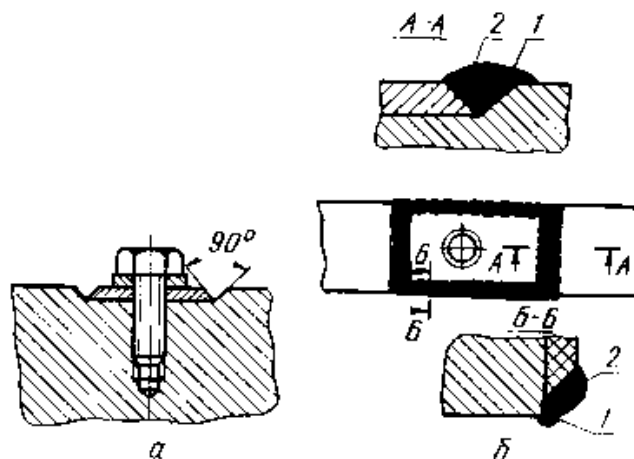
Заварка тріщини, що проходить через оброблену поверхню, з постановкою пластини:
